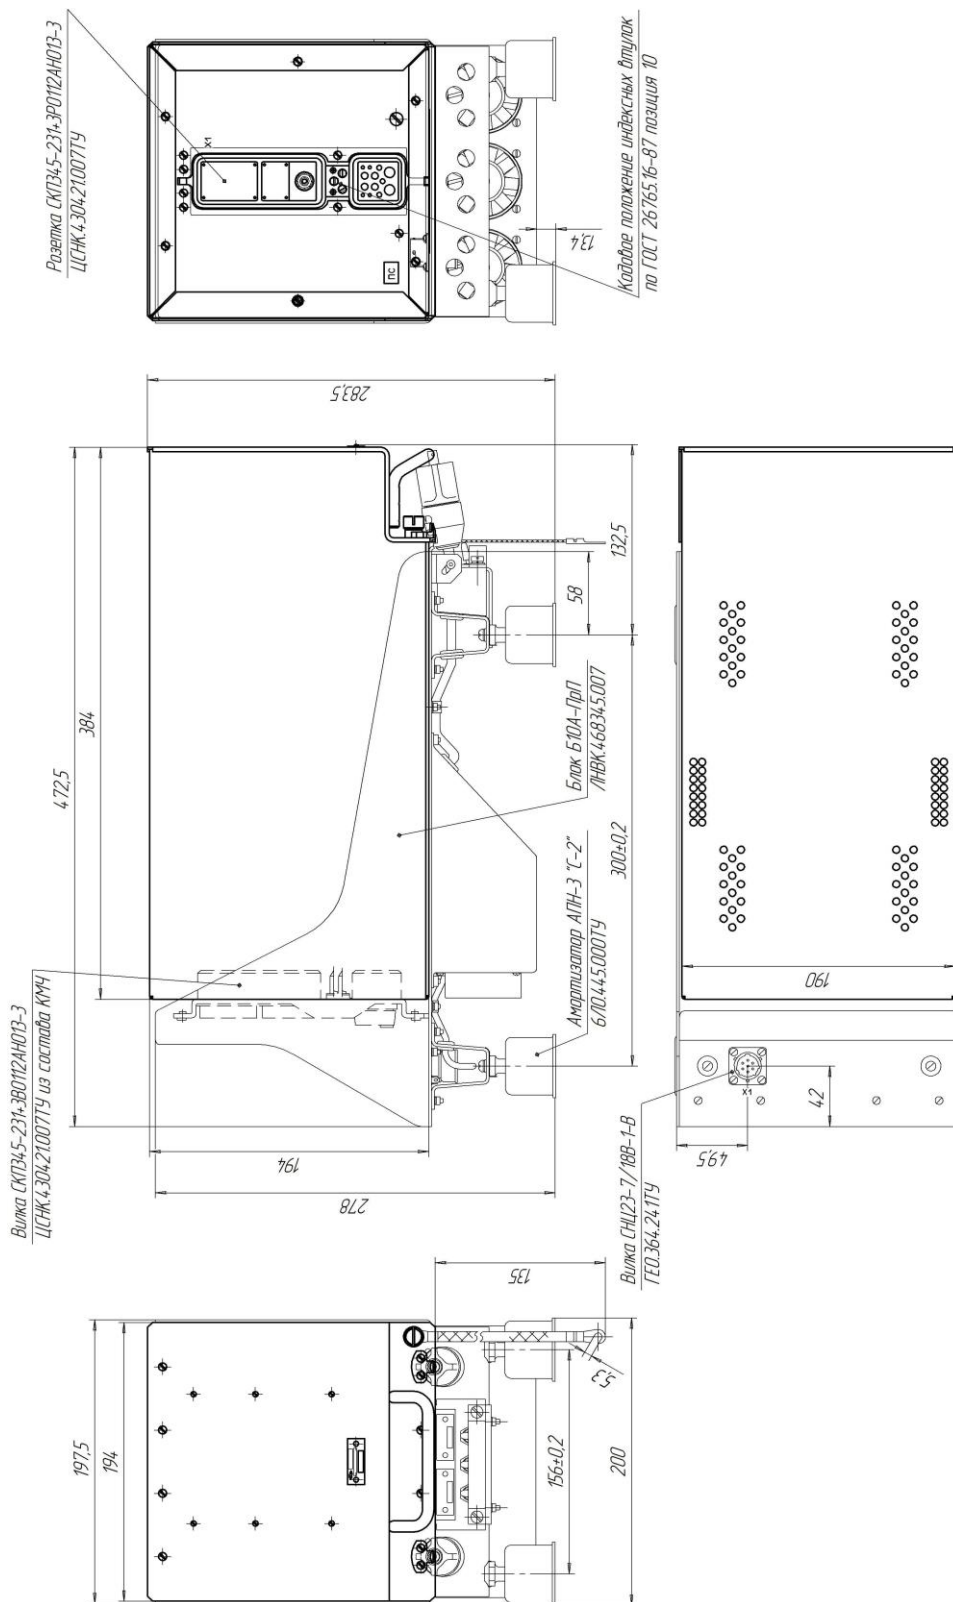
Габаритный чертеж блока Б1А-ПрП на блоке Б10А-ПрП
